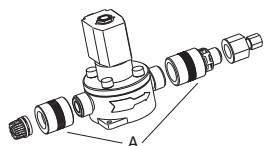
ЭМК OCD-162-5, -10: Сборочный чертёж
